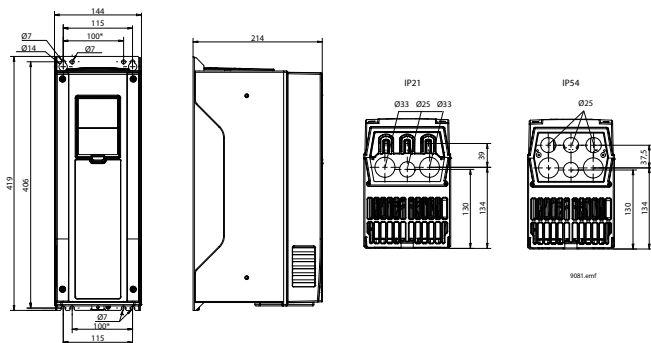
Dimensões do inversor de CA Praxi, MR5, montagem na parede
